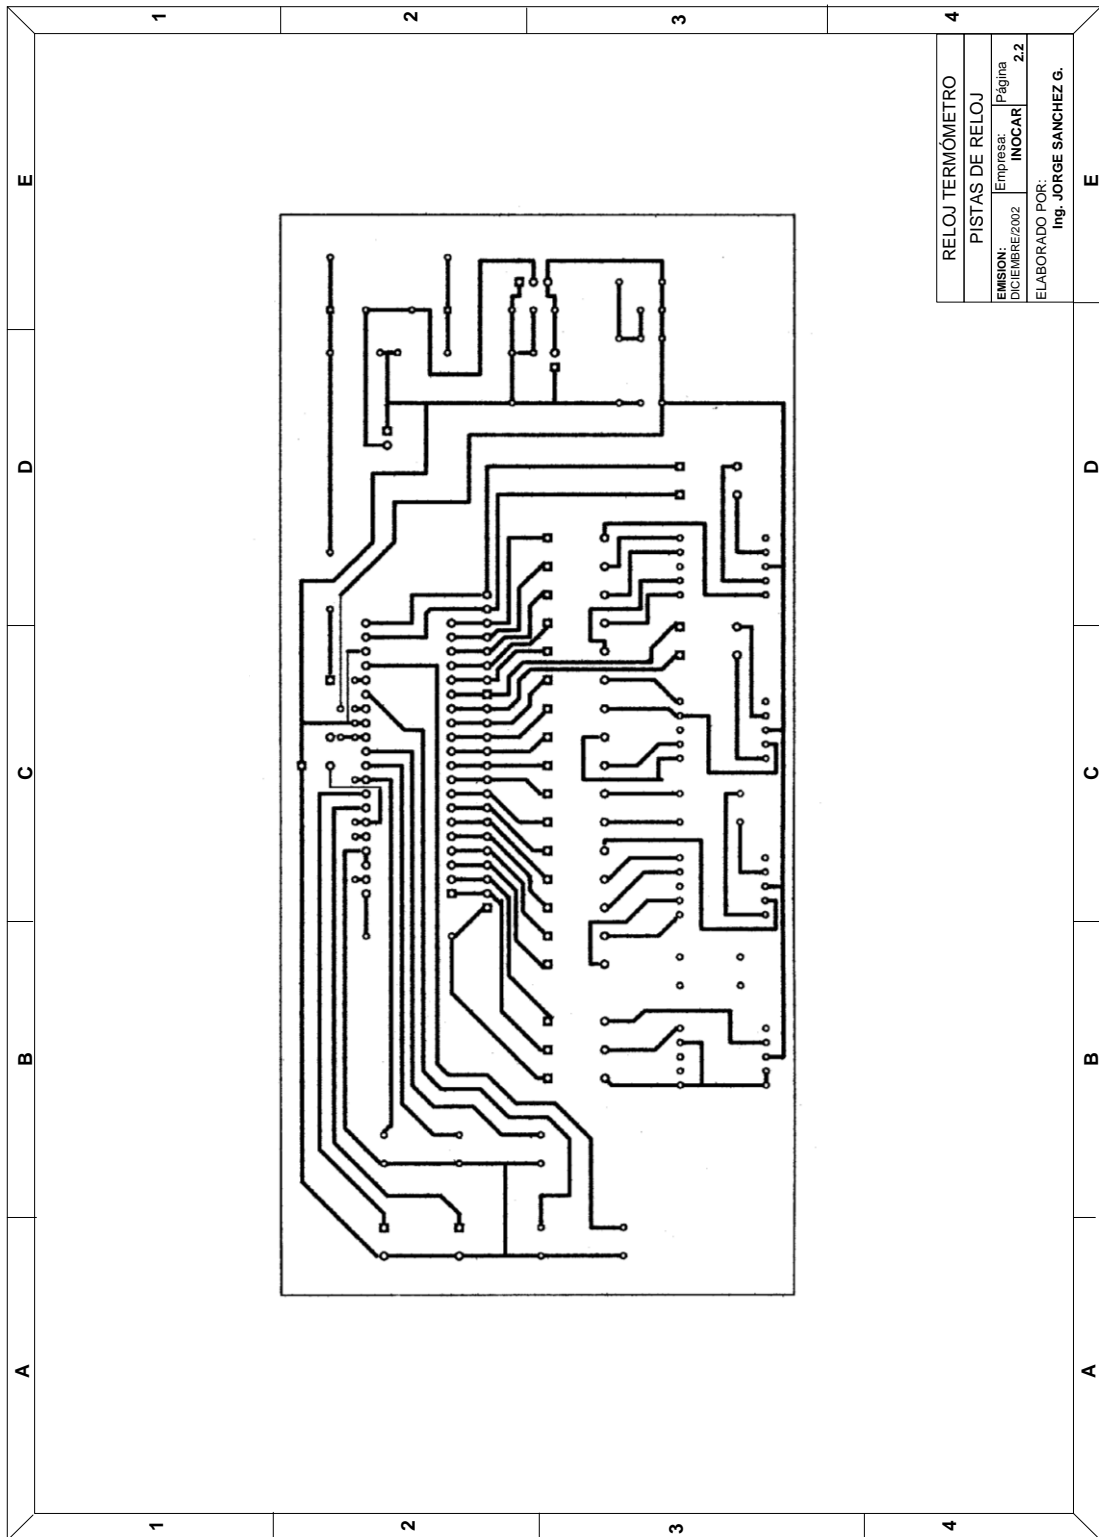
Tarjeta de reloj (diagrama de pistas lado de soldadura)
